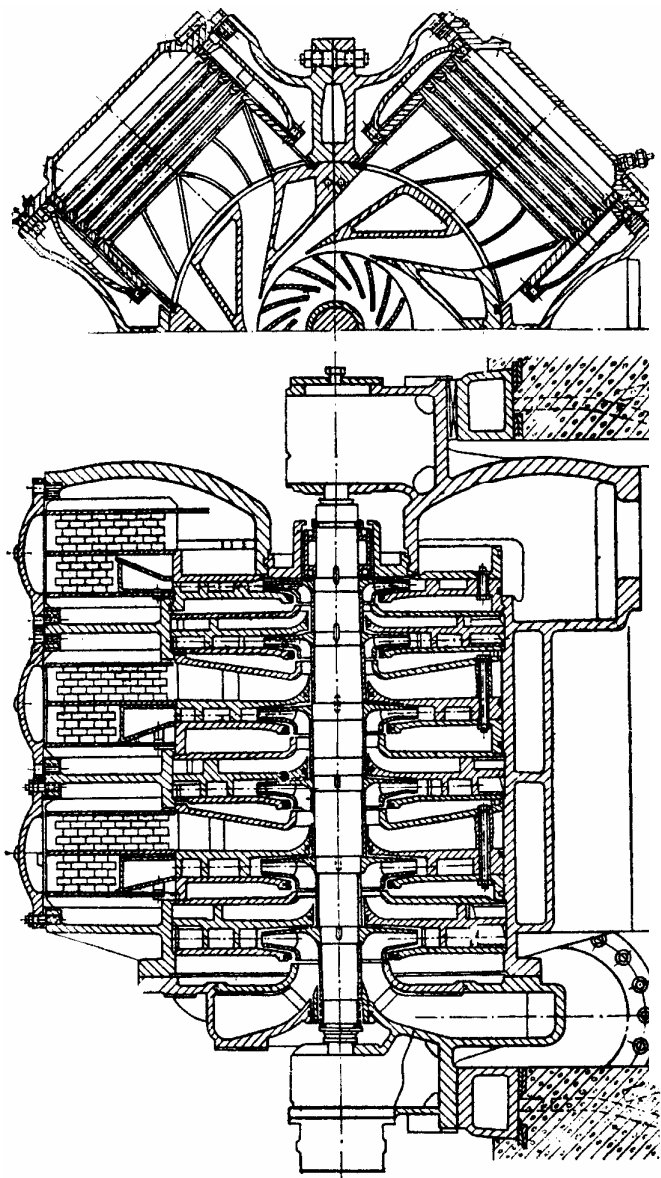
Центробежный компрессор со встроенными охладителями
